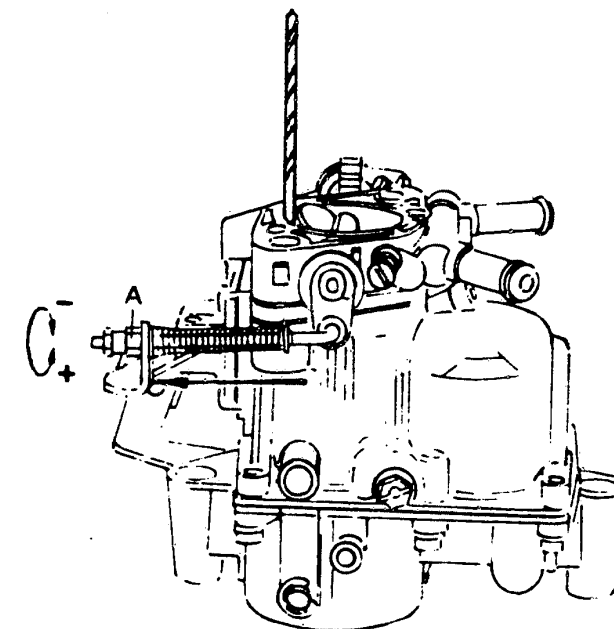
Einstellung des Beschleunigerpumpenhubes. Schraube A lösen, 2,4-mm-Bohrer zwischen Drosselklappe und Gehäuse schieben, Schraube A bis zum Kontakt mit Hebel anziehen.
